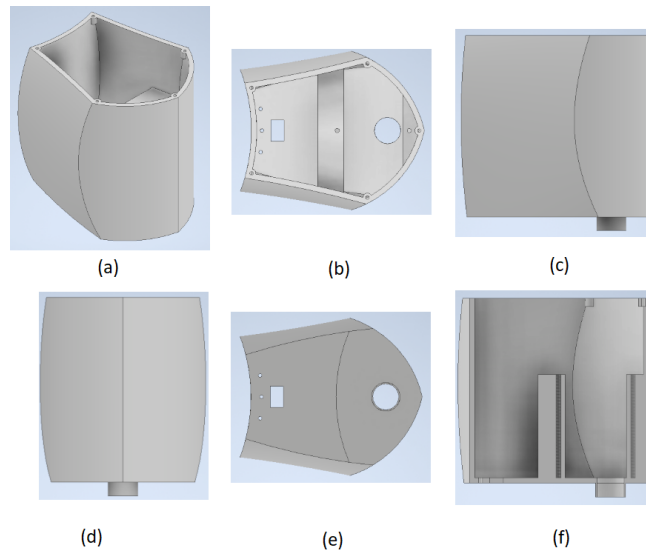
Tapa cabeza. (a) General, (b) Superior, (c) Frontal, (d) Derecha, (e) Inferior, (f) Frontal seccionado
